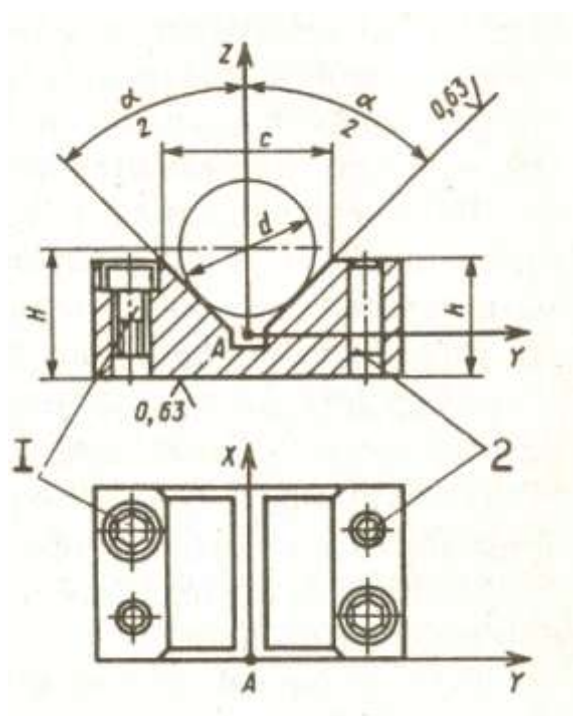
Призма для установки небольших заготовок с базированием по обработанным поверхностям
